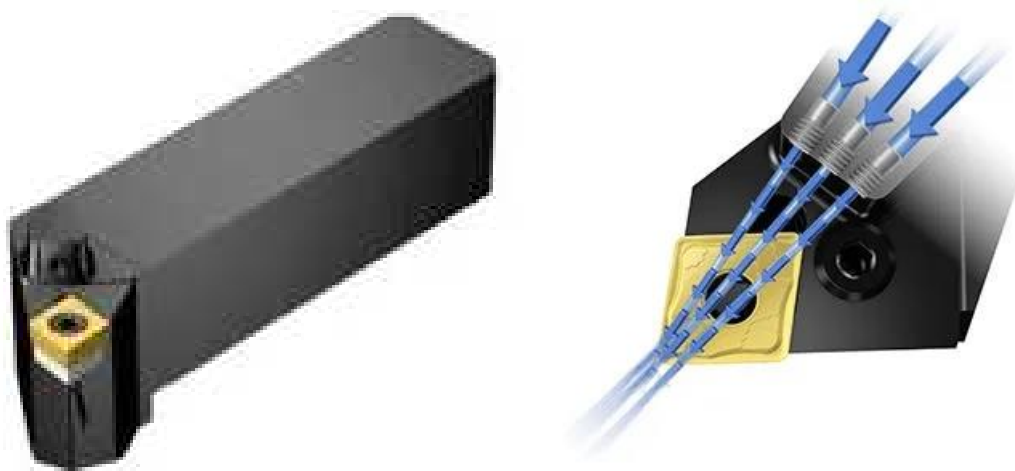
Державка SANDVIK T-Max P для ромбічних пластин
